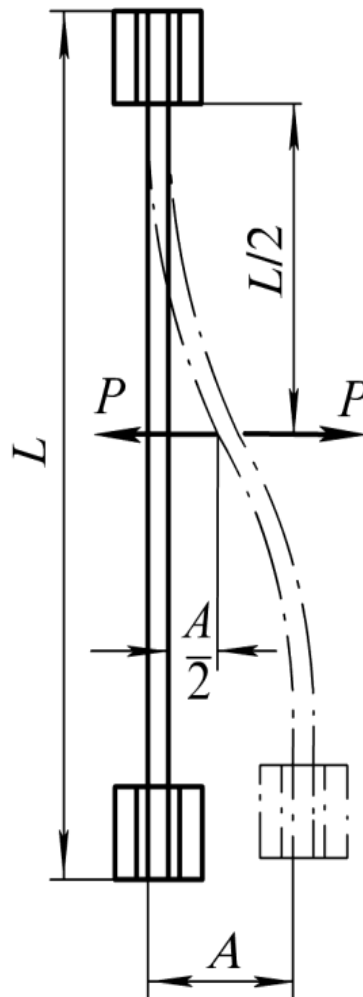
Розрахункова схема підвіски решітного стану
